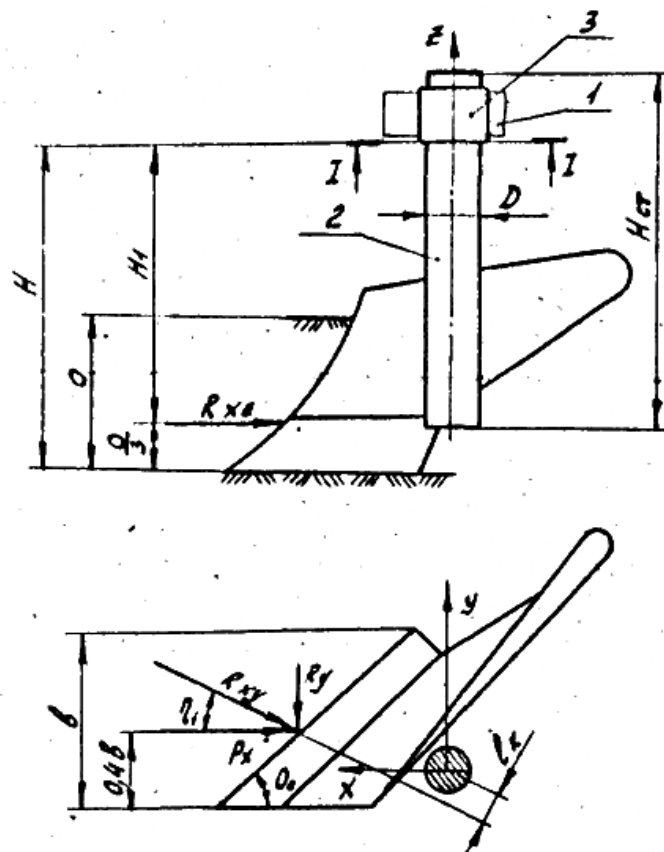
Схема для розрахунку на міцність стійки корпуса плуга
